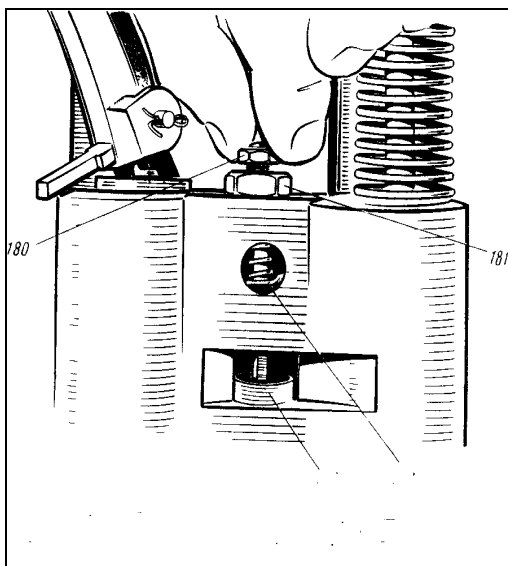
180—контргайка штока; 181—верхняя упорная тарелка пружины
